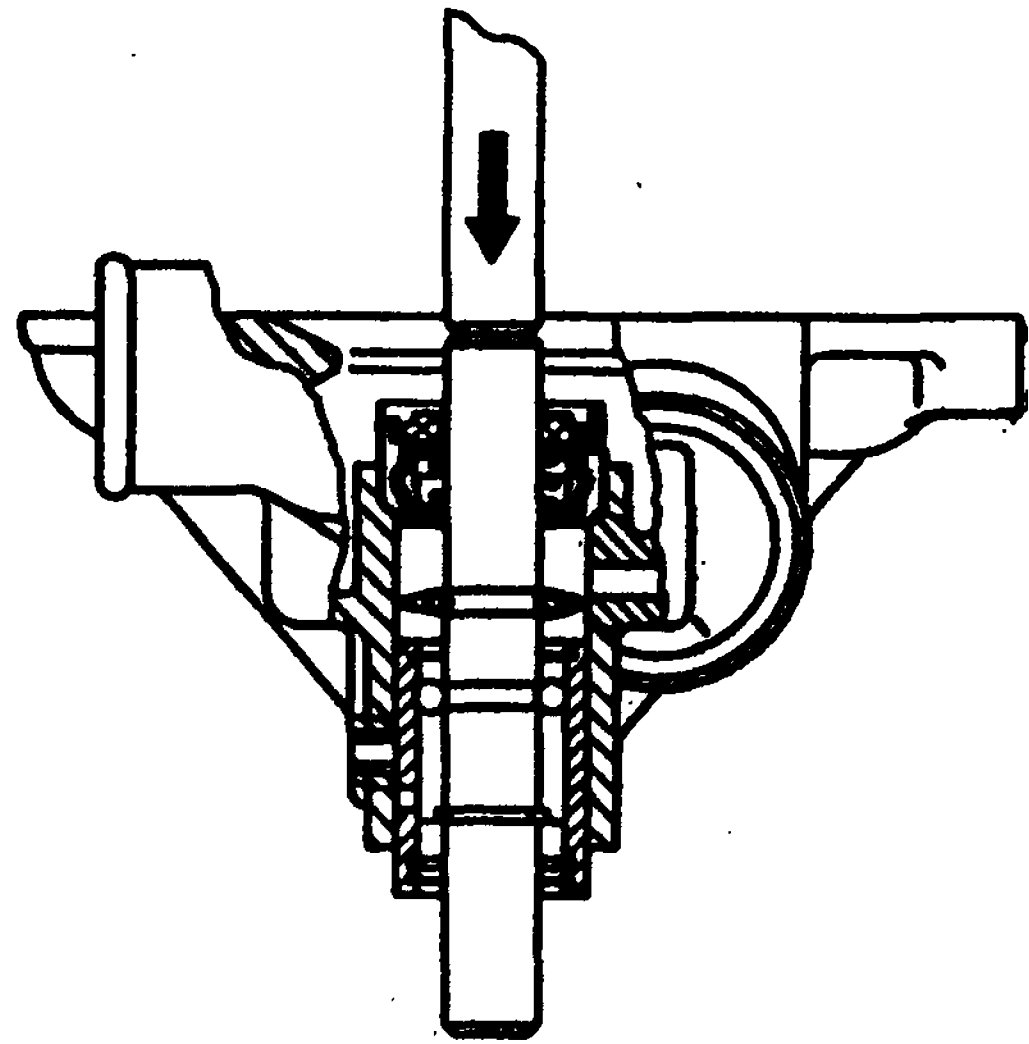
Выпрессовка подшипника с валом водяного насоса
